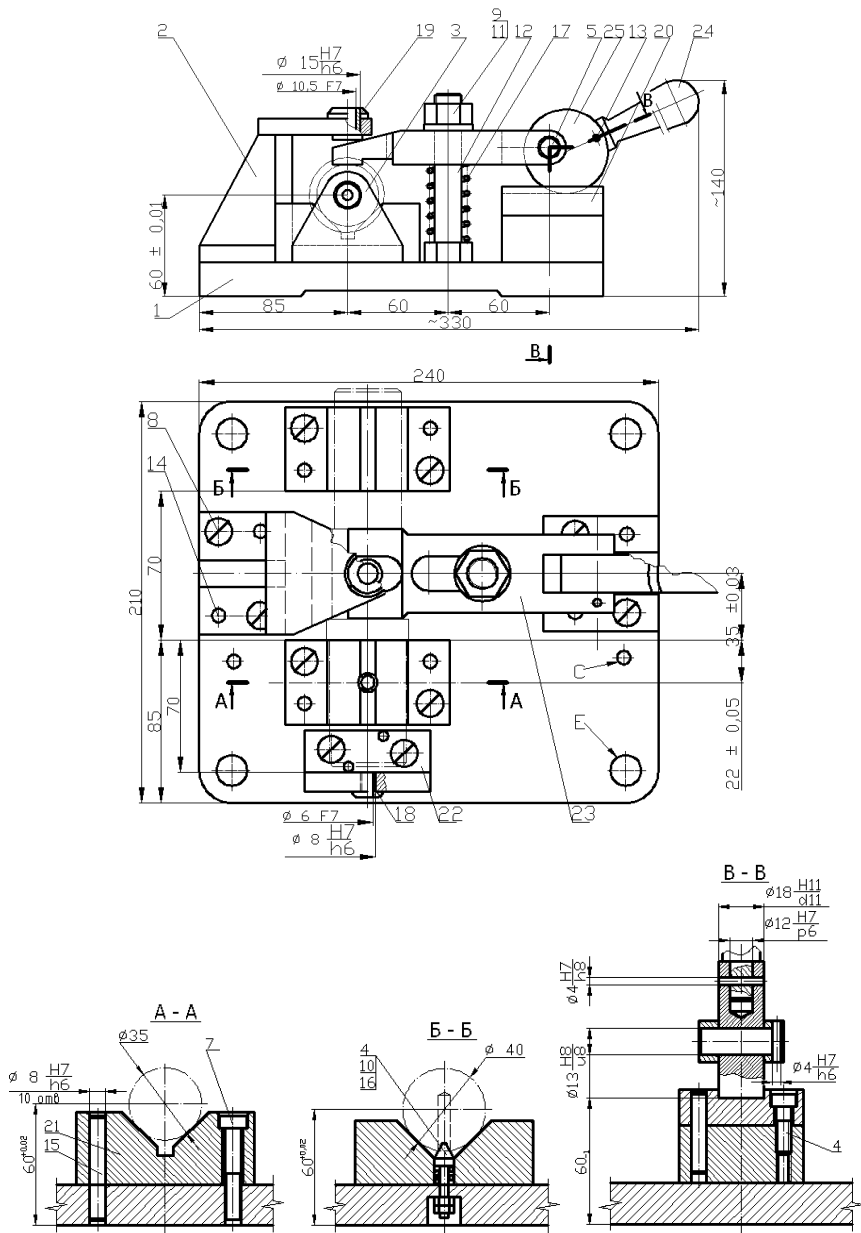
Чертеж спроектированного приспособления для сверления отверстий в деталях типа валов
